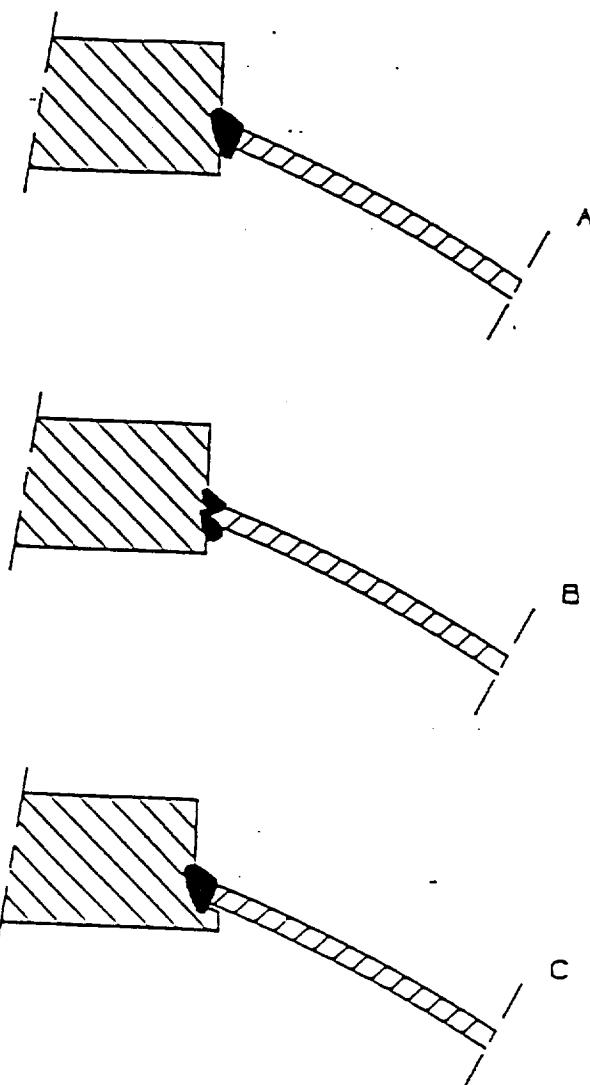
ОБРАЗЦЫ ПРИВАРЕННЫХ ПЛАСТИН КРЕПЛЕНИЯ
